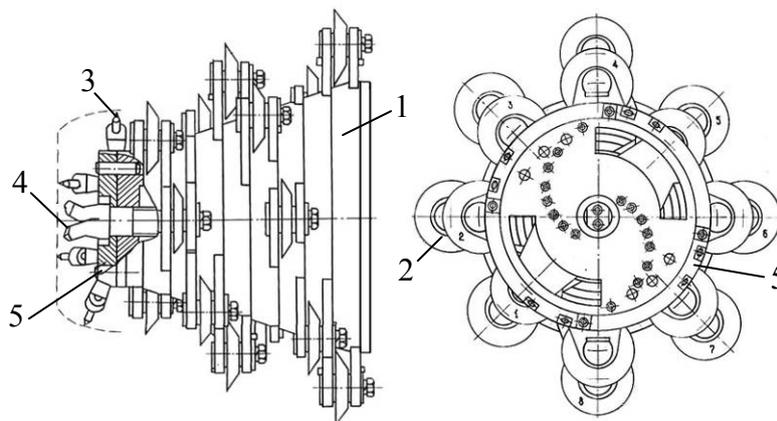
Базовая конструкция коронки проходческого комбайна с дисковым инструментом
